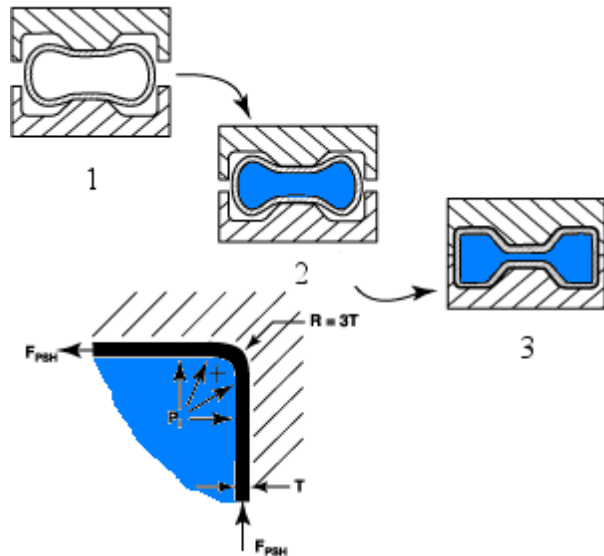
Výrobky vhodné pro nízkotlaký hydroforming [6], [34]
